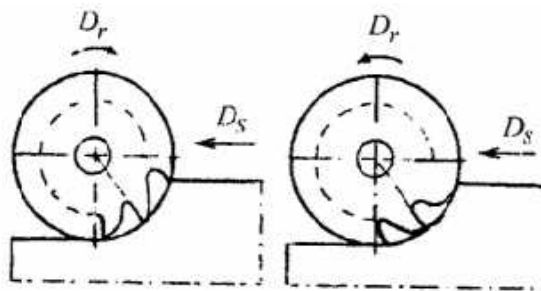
Схема зустрічного (а) і попутного (б) фрезерування [2]
